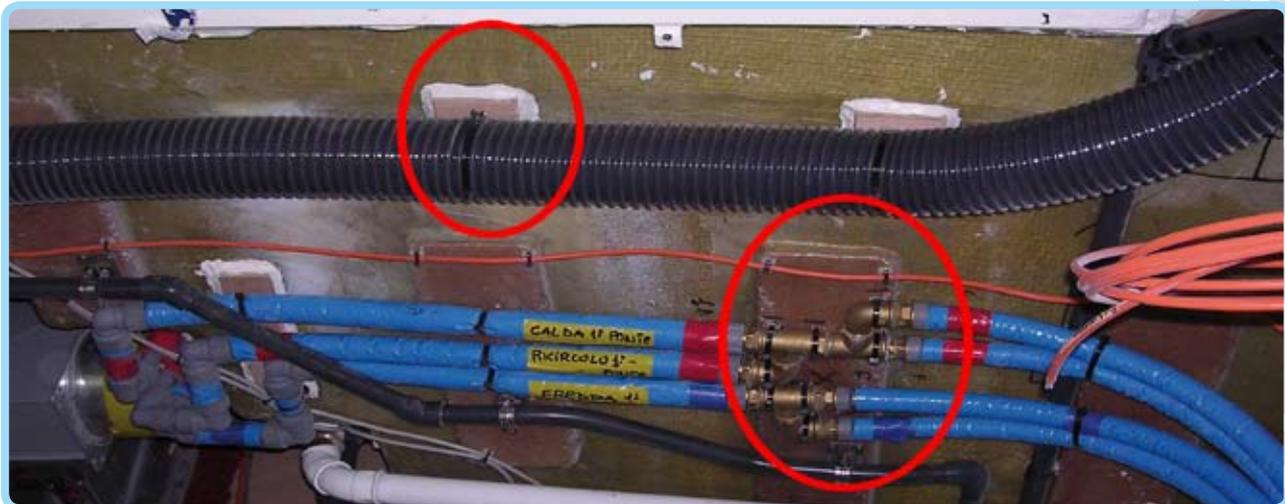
Impianti tecnologici: particolare degli impianti a servizio dell'imbarcazione.
